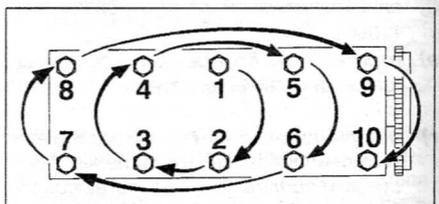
Последовательность затяжки болтов крепления головки цилиндров (двигатели 1.9 л)
